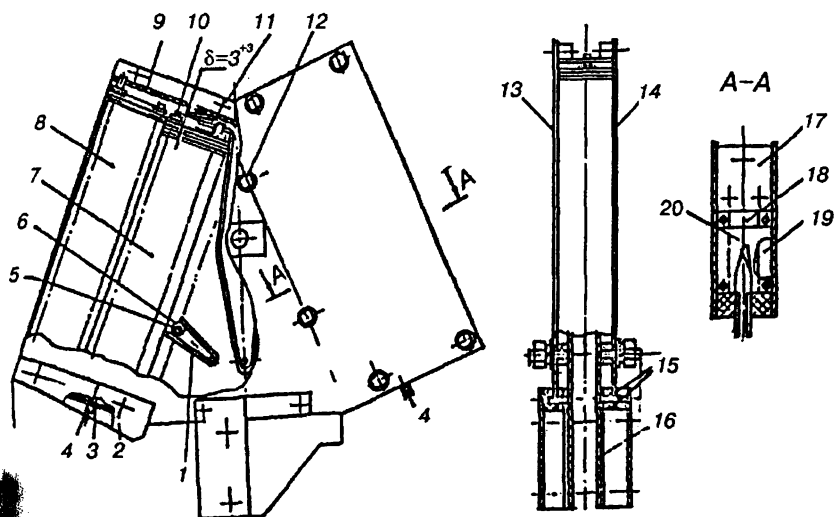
Дугогасительная камера выключателя ВАБ-49
